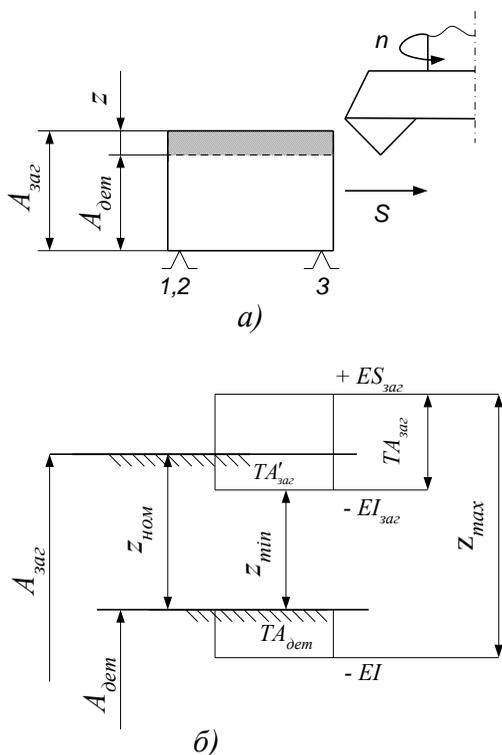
Схема торцевого фрезерования плоскости и расчетная схема для определения охватываемого размера заготовки
